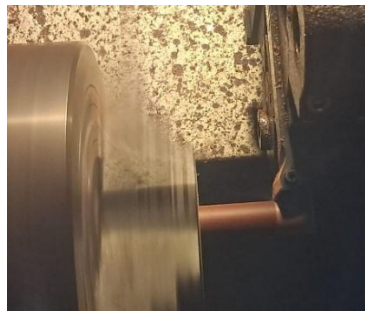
LEADWELL CNC Lathe Fanuc Oi Tc
